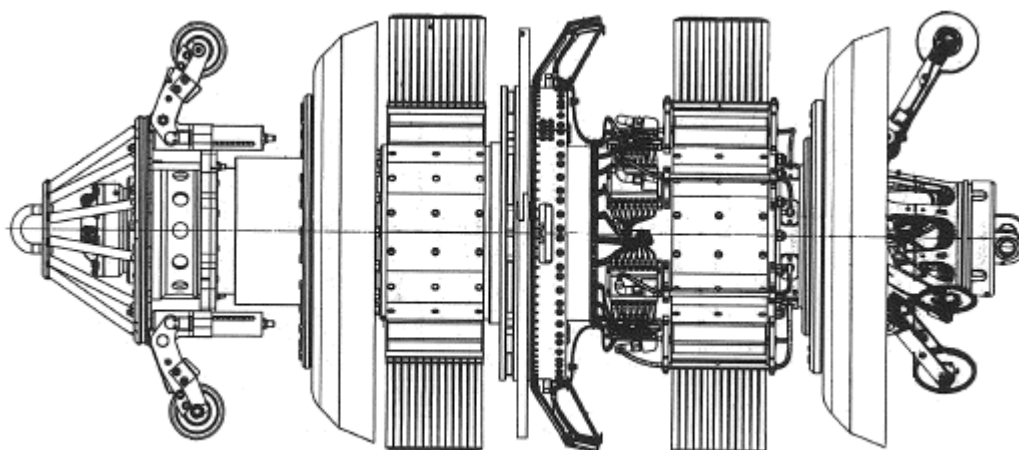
Чертеж общего вида дефектоскопа внутритрубного магнитного 42-MCK.01-00.000-01 и 48-MCK.01-00.000-01
